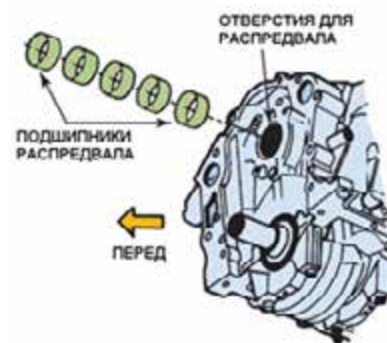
Двигатель с распределительным валом в блоке цилиндров поддерживает распределительный вал на подшипниках втулочного типа, запрессованных в отверстия блока цилиндров; источник: *Pearson Education, Inc.
